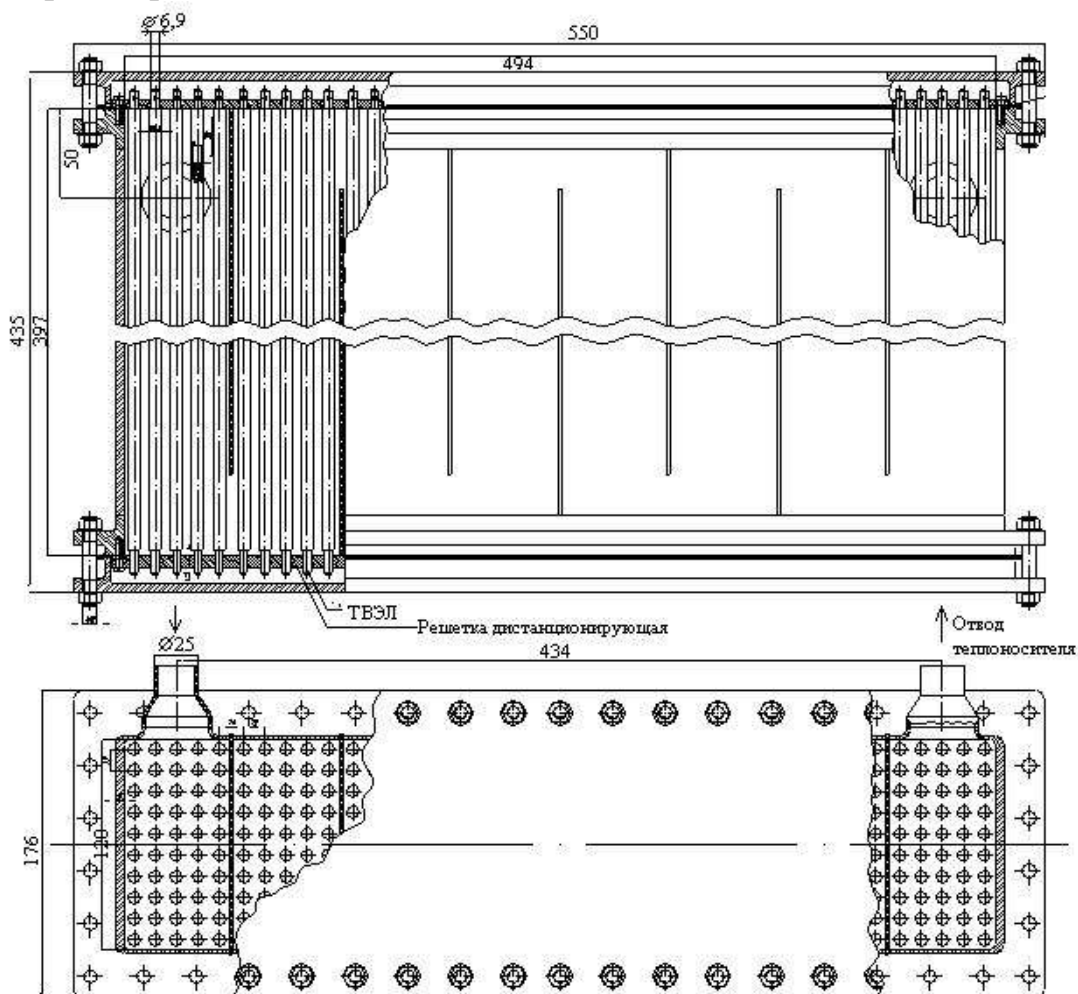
Конструкция корпуса реактора РУ МАРС с установленными твэлами
